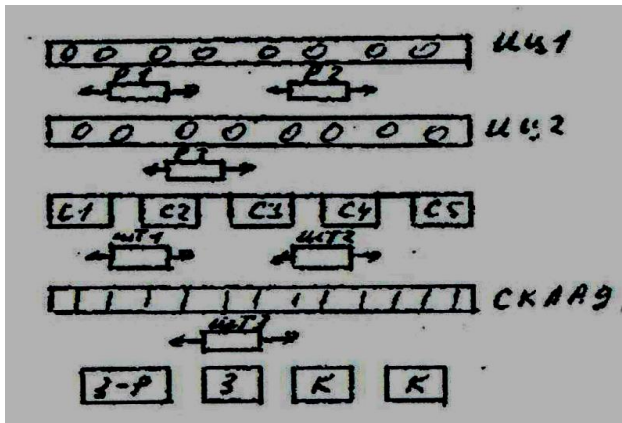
Зразкова схема ГВС з інструментальним складом для заготовок і деталей
